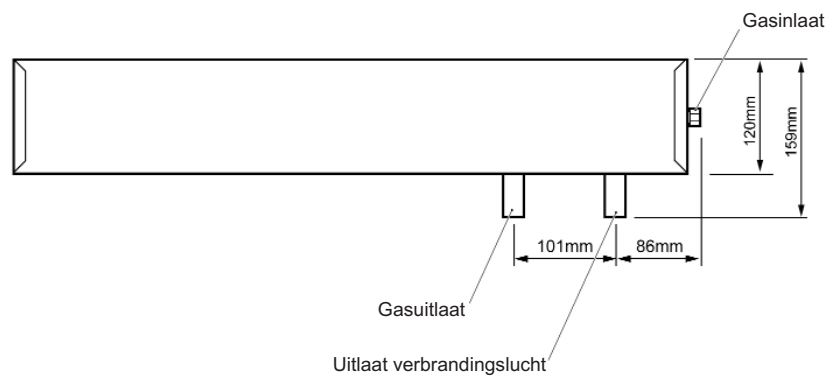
Afmetingen: Vooraanzicht bij installatie in het voertuig
